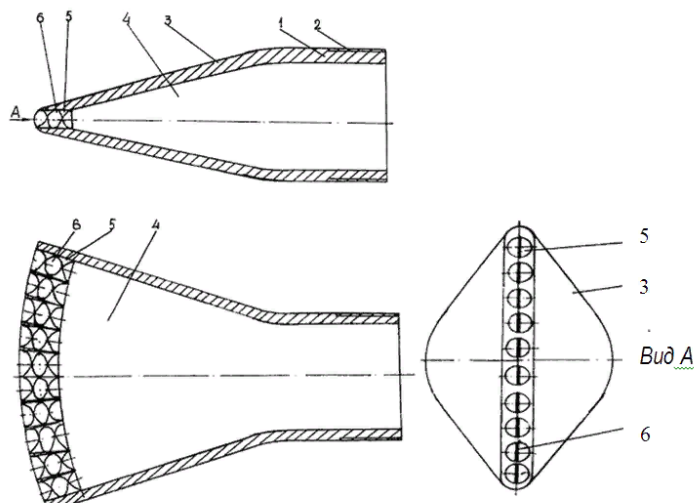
Схема веерной дождевальной насадки-активатора: 1 – цилиндрический корпус; 2 – соединительная резьба; 3 – веерный насадок; 4 – сужение в вертикальной плоскости; 5 – водовыпускные отверстия; 6 – шнековые направители
